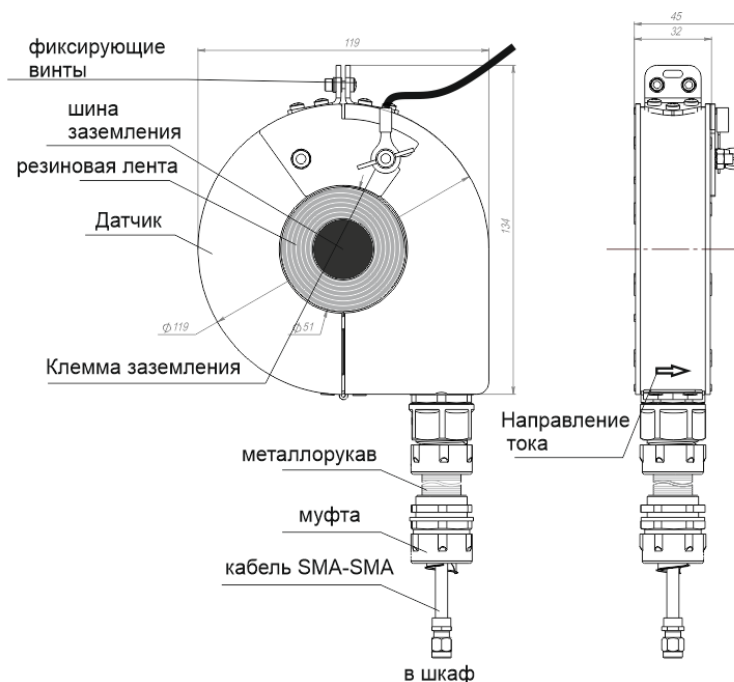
Общий вид и габаритные размеры датчика частичного разряда высокочастотного тока
